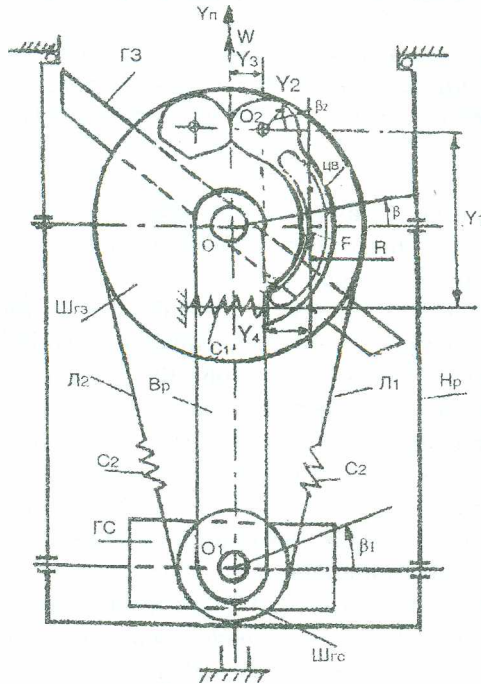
Кінематична схема механізму натягання металевої стрічки
